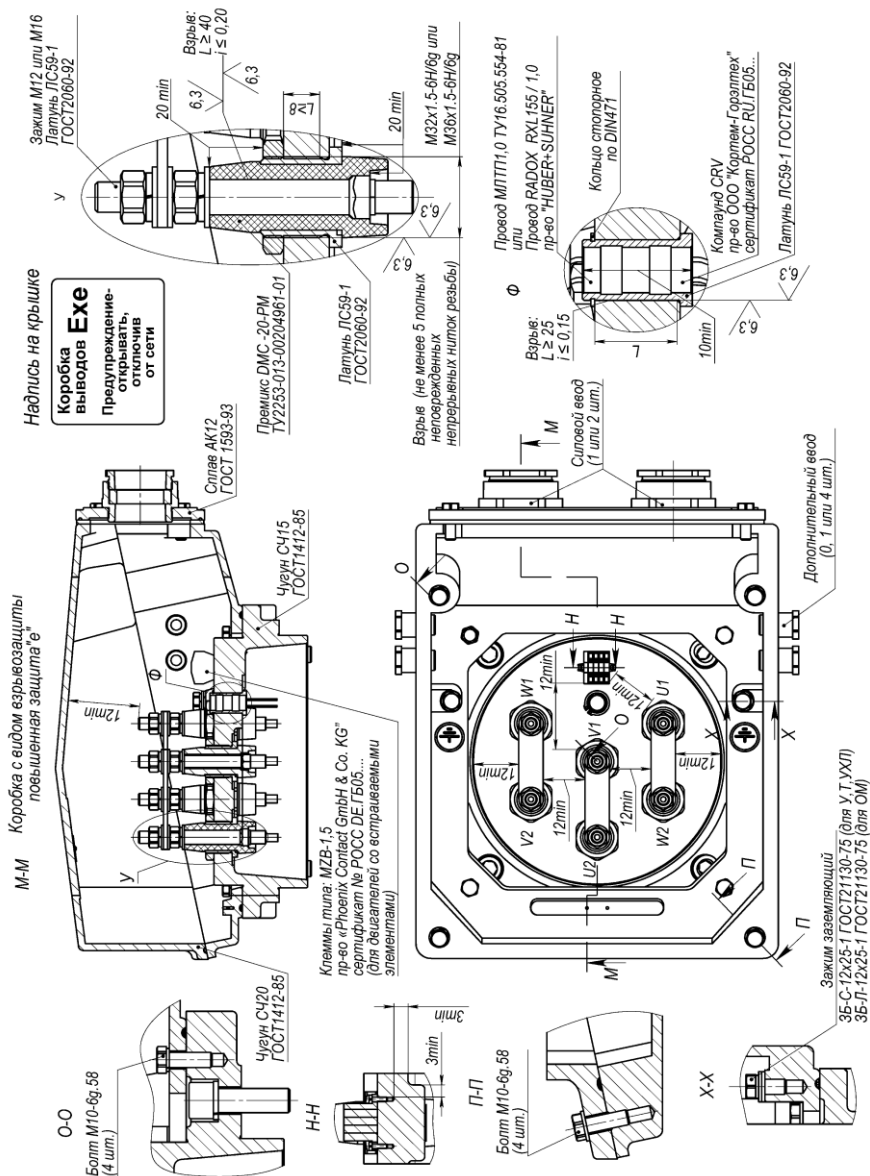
Чертеж взрывозащиты коробки выводов «е»
